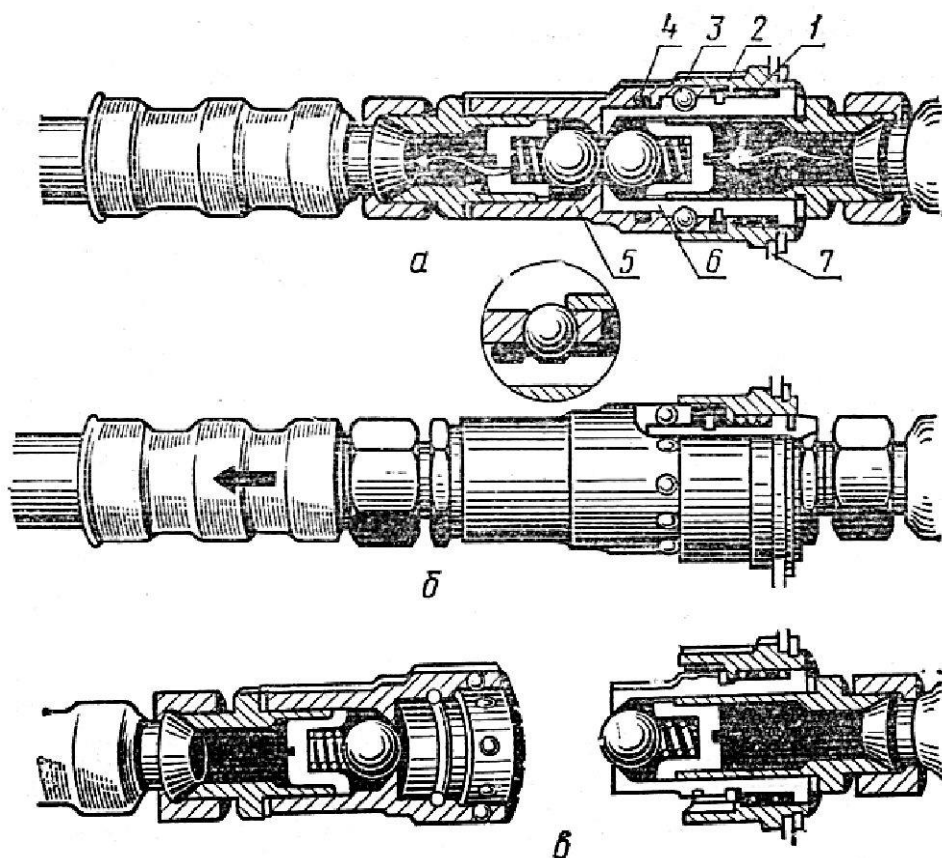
Разрывная муфта: *а* - в рабочем положении; *б* - в начале размыкания; *в* - в разомкнутом положении; 1 - пружина фиксатора; 2 - обойма фиксатора; 3 - шарик замка; 4 - резиновое уплотнительное кольцо; 5 - левый корпус клапана; 6 - правый корпус клапана; 7 - кронштейн
